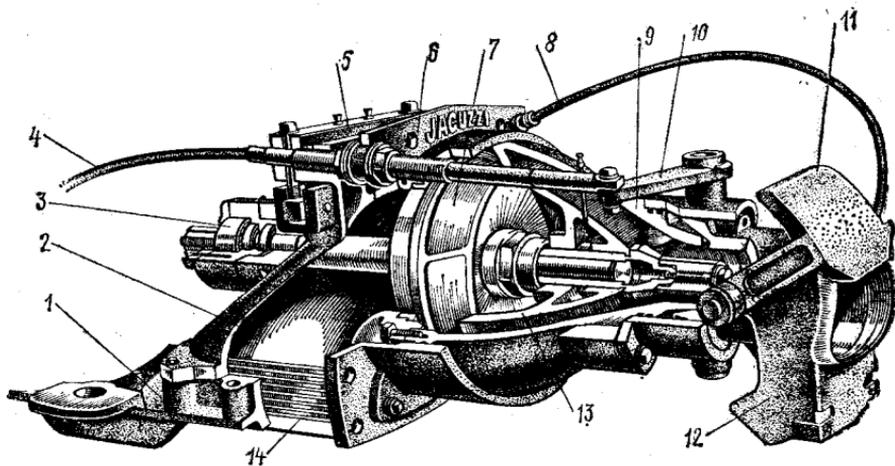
Промышленный образец водометного движителя для быстроходных катеров с насосом смешанного типа.
